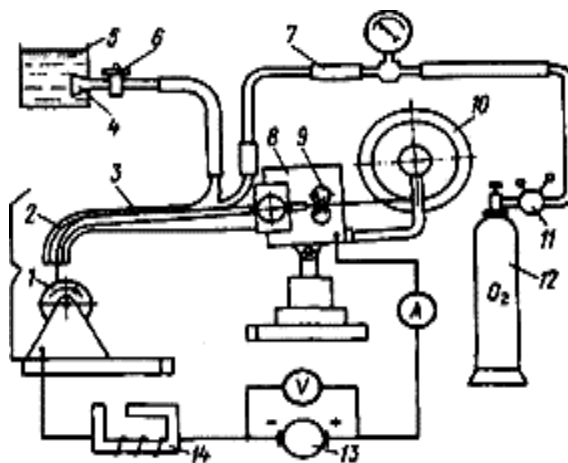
Схема установки для вібродугового наплавлення в газорідному середовищі
